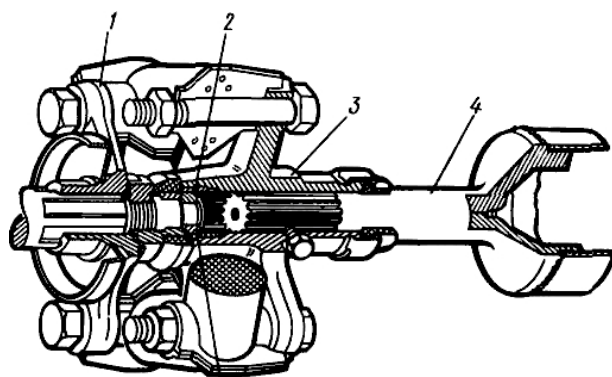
Карданная передача с упругим полукарданным шарниром: 1, 3 — фланцы; 2 — втулка; 4 — карданный вал
